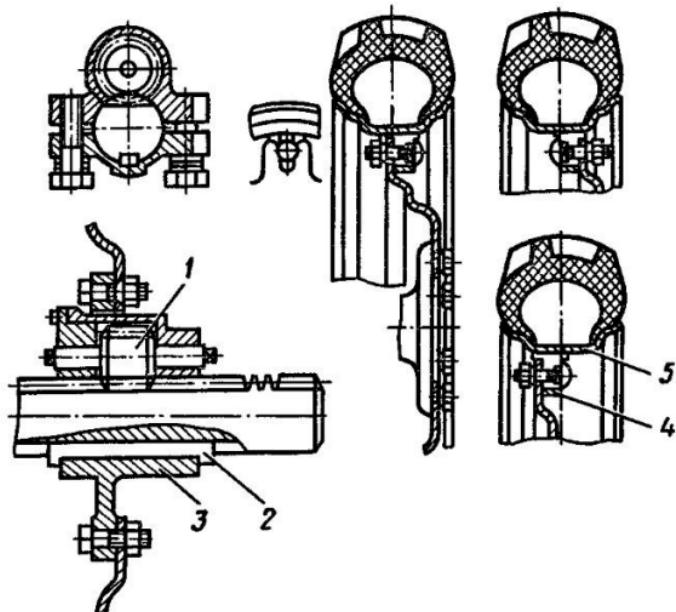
Ступица ведущего колеса трактора МТЗ-80:
